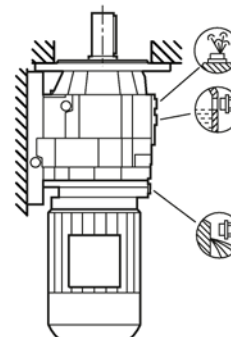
Монтажные положения для цилиндрического редуктора DB/ZB в исполнении на лапах / с фланцем, типоразмер 29
